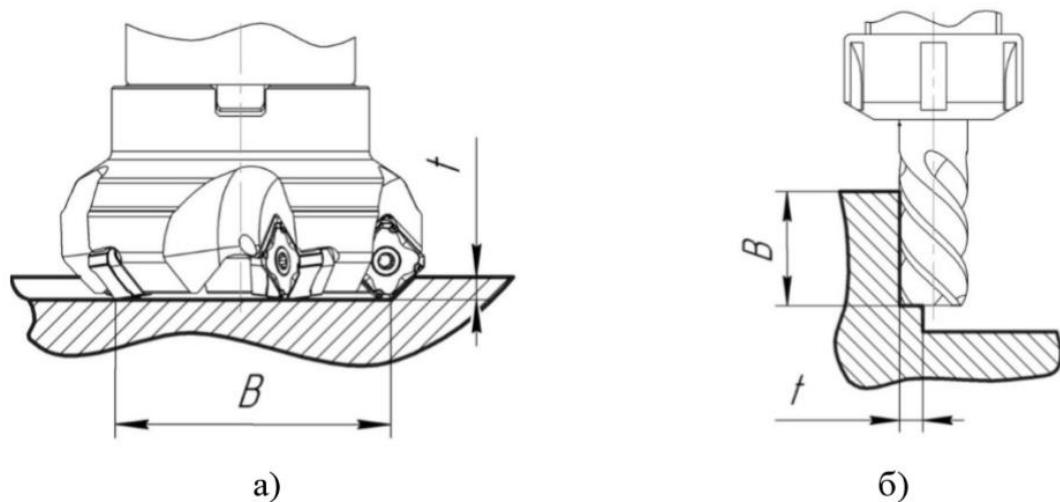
Фрезерування: а) торцевою фрезою б) кінцевою фрезою, де
